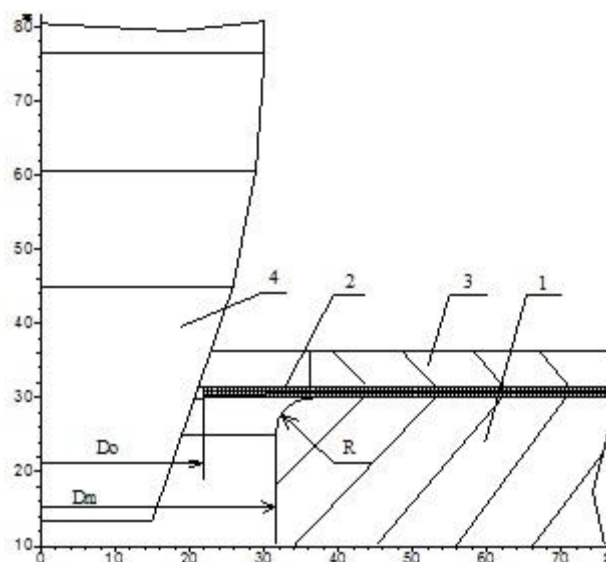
Схема процесса отбортовки с геометрическими размерами.
